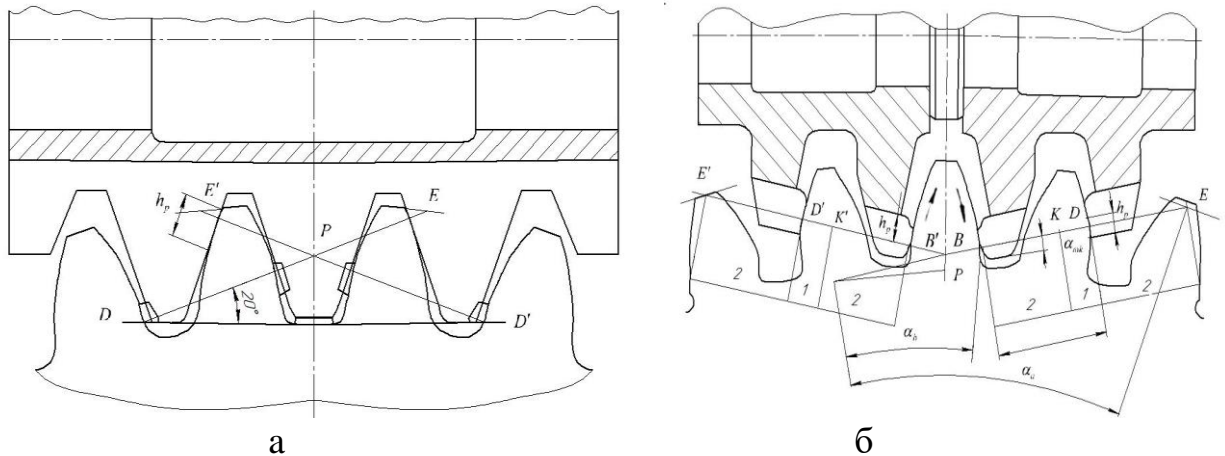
Визначення сумарного периметра одночасно ріжучих кромок: а - для черв'ячної фрези з роздільною схемою формоутворення; б - для стандартної фрези
